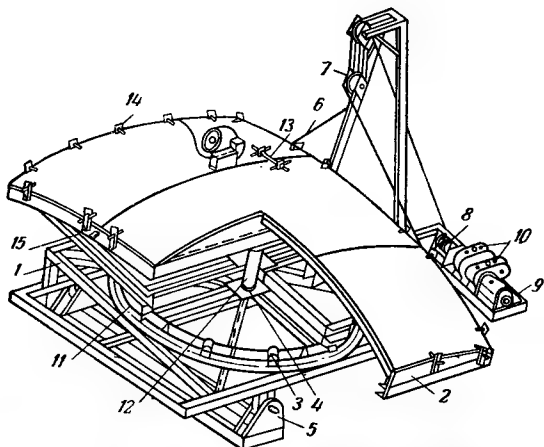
Манипулятор — вращатель для монтажной сварки шарового резервуара
